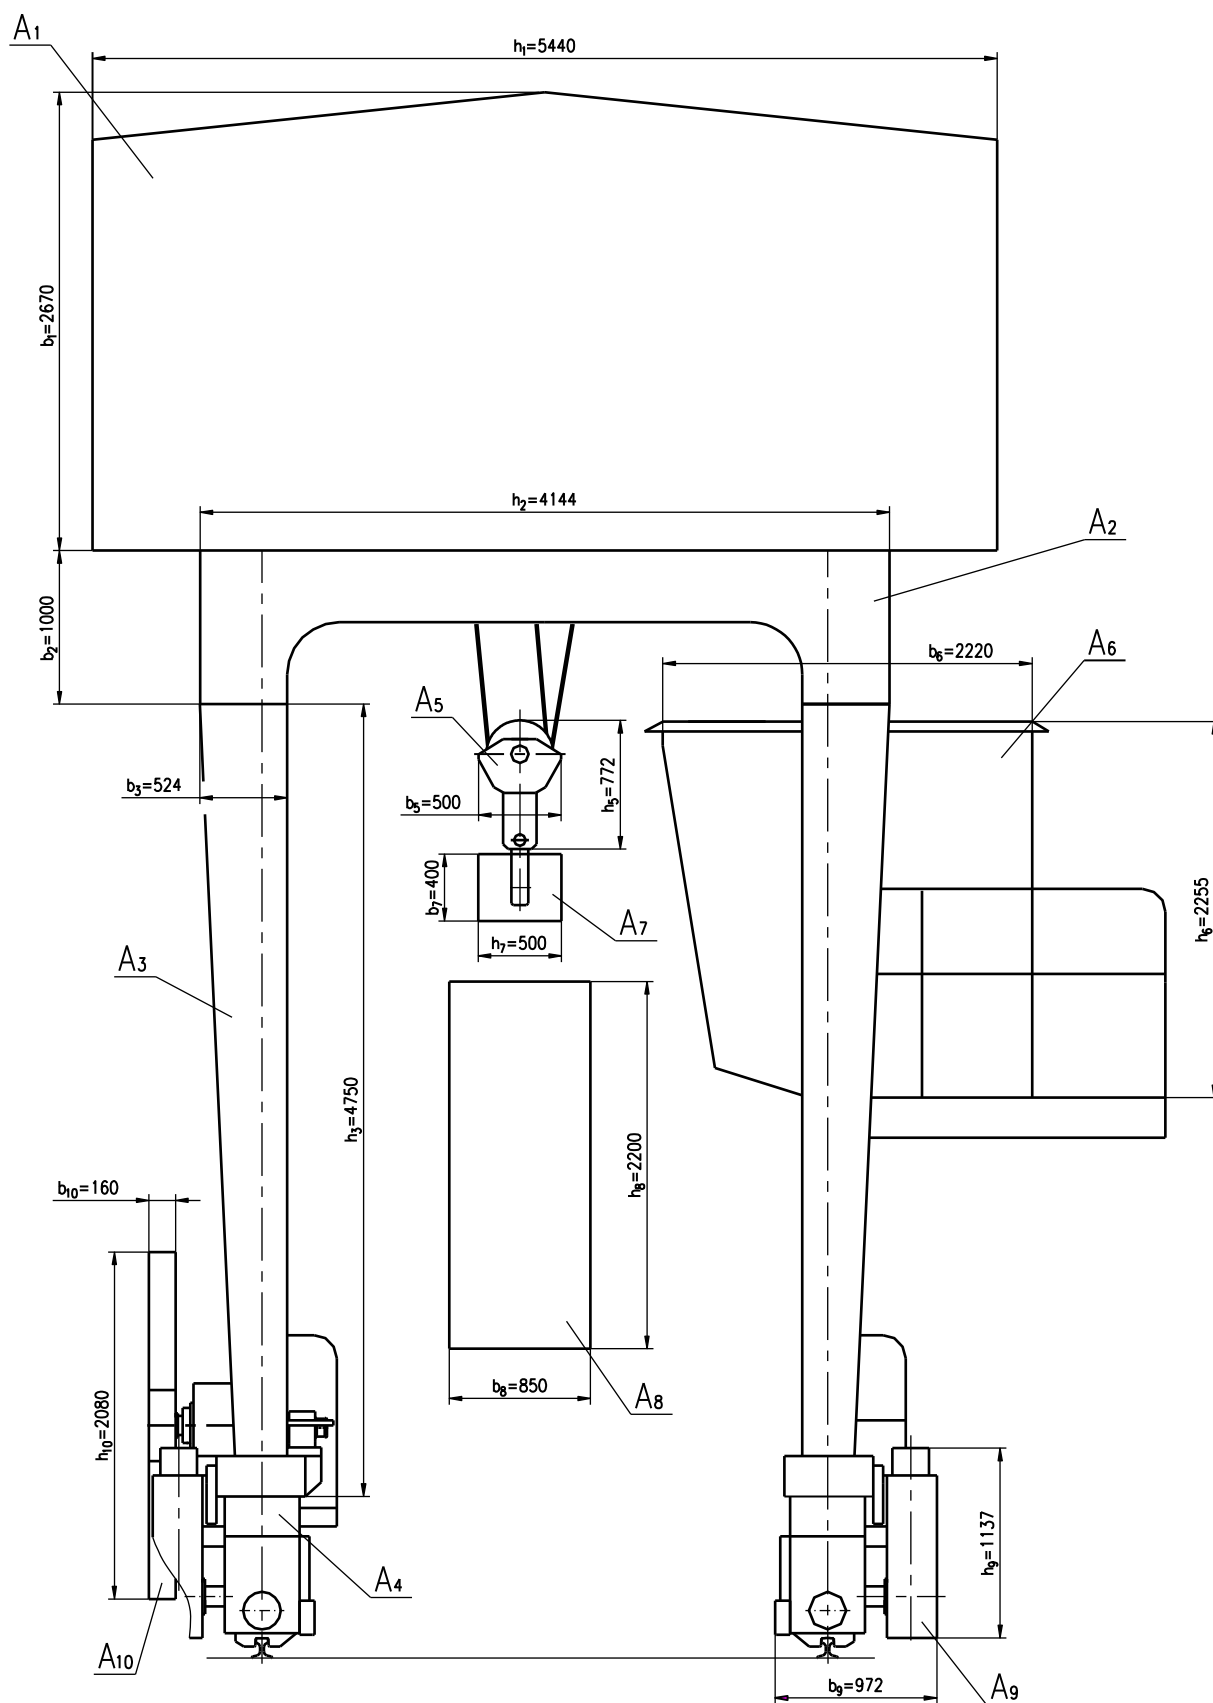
Схема до розрахунку вітрового навантаження на кран при вітрі вздовж шляху крана
